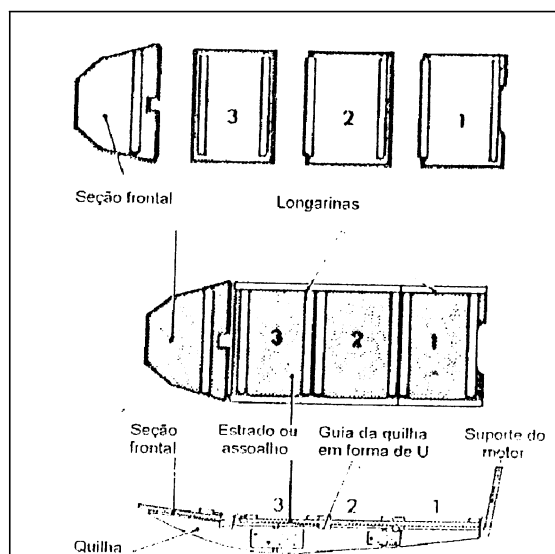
Esquema de montagem do bote de reconhecimento Sillinger
